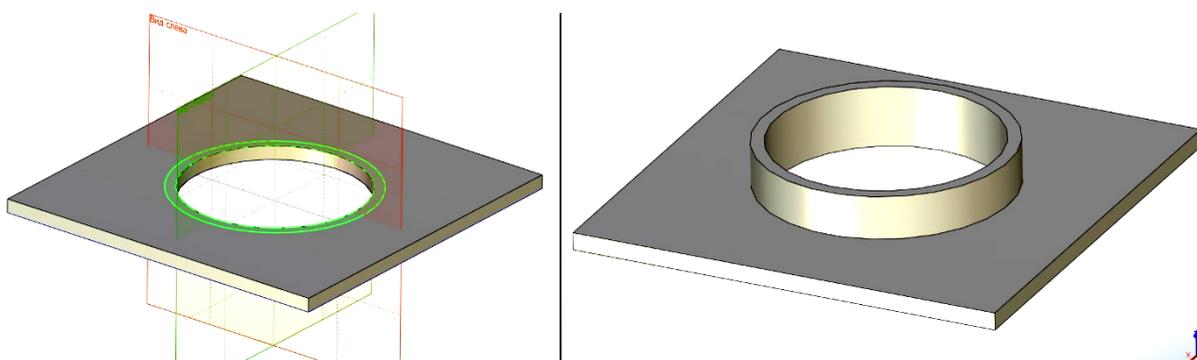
3D-модель верхней пластины корпуса ОПУ
